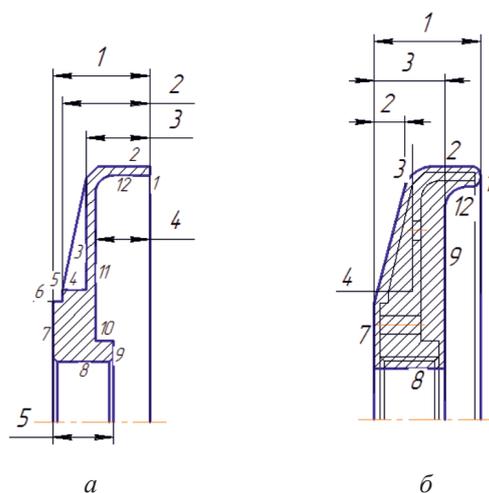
Эскиз геометрической модели детали (а) и заготовки (б)
